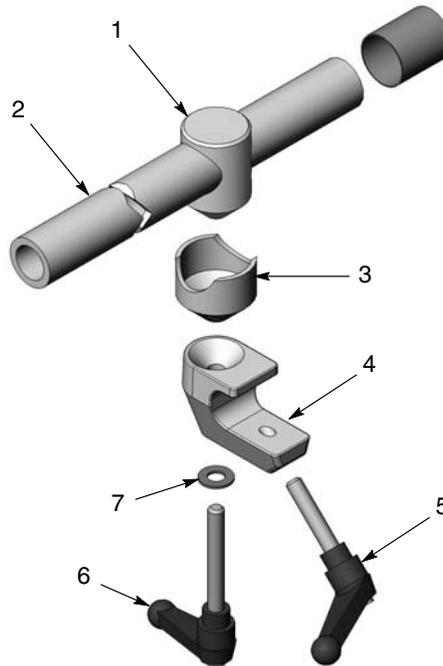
Barra de suporte para pistolas com barra de suporte
